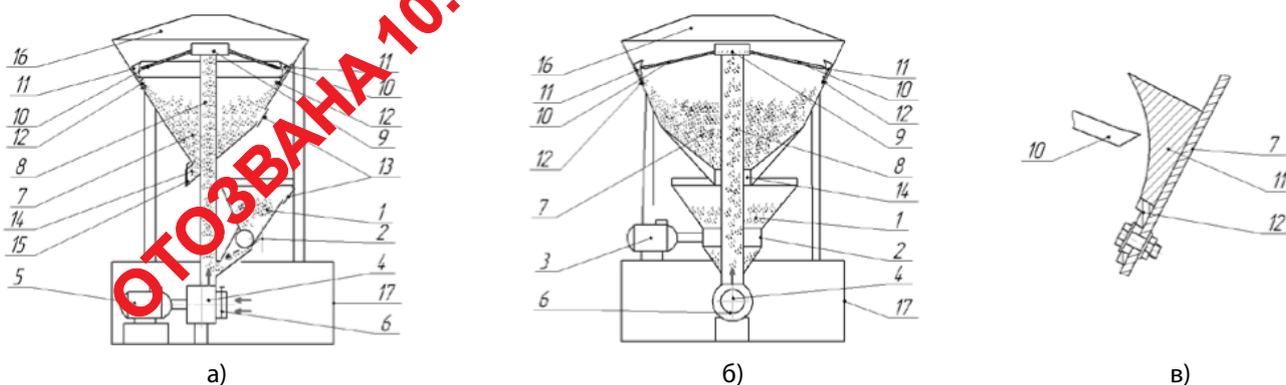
Пневматический скарификатор: а) – общий вид с приводом на вентилятор; б) – общий вид с приводом на катушечный с инжектором дозатор; в) – регулируемая опора цилиндрической наждачной поверхности; 1 – загрузочный бункер; 2 – катушечный с инжектором дозатор; 3 – мотор-редуктор; 4 – вентилятор; 5 – электродвигатель; 6 – жалюзийная заслонка; 7 – бункер скарифицированных семян; 8 – шахтная труба; 9 – распределительная головка; 10 – семяпроводы; 11 – наждачная поверхность; 12 – опоры; 13 – смотровые окна; 14 – выгрузное окно; 15 – заслонка; 16 – матерчатая крышка; 17 – рама
